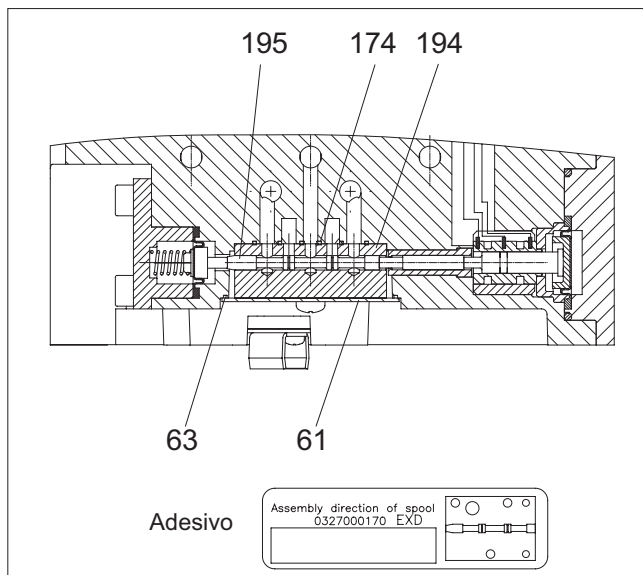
Conjunto da válvula de carretel, ND9200, ND7200 e ND9300
